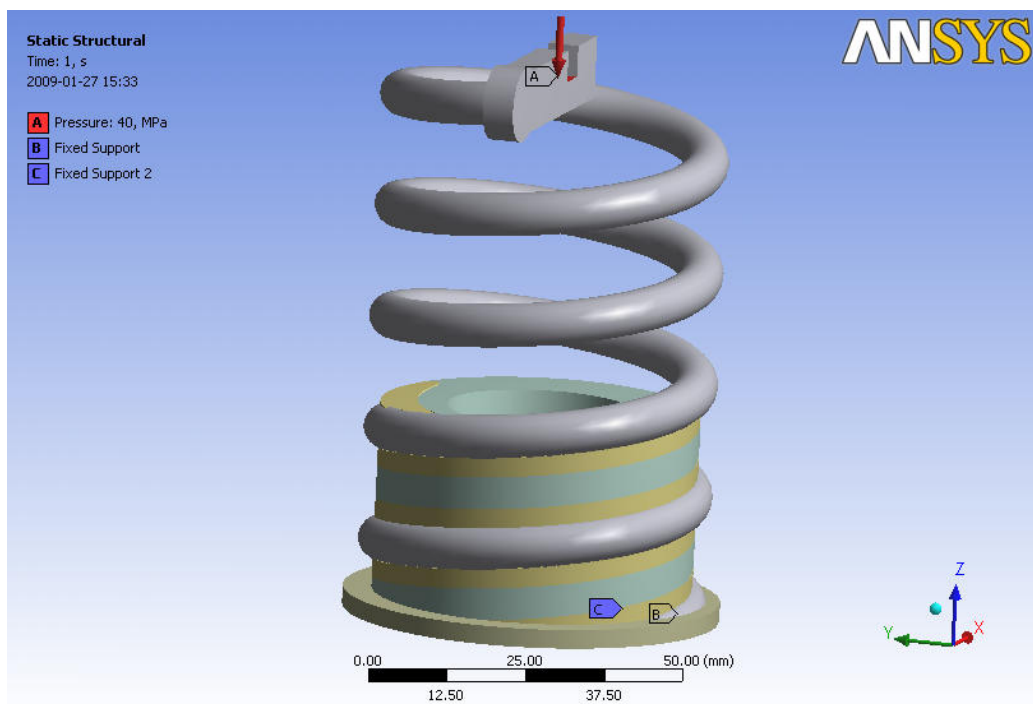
Nowa konstrukcja wkrętki mocującej
